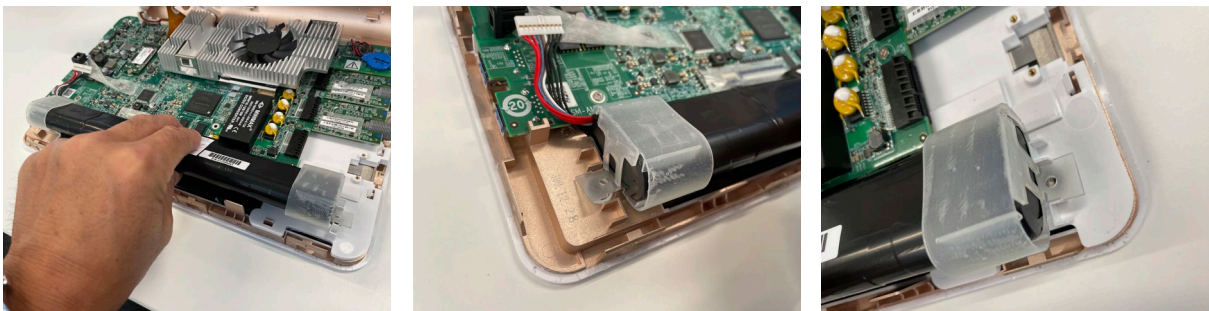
Recolocación de la batería con las tapas de la batería en el dispositivo
